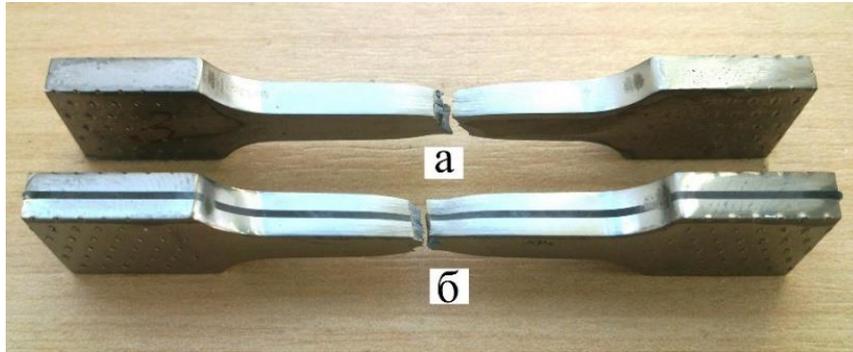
Внешний вид поверхности разрушенного образца, соединенных между собой листов, после испытания на растяжение вдоль сварного соединения:
